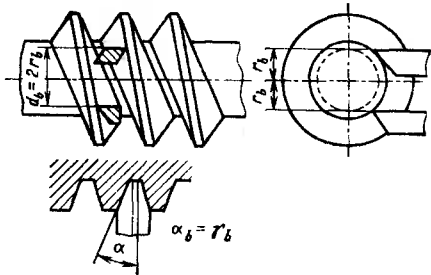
Схема установки резцов для нарезания правого червяка Z1
